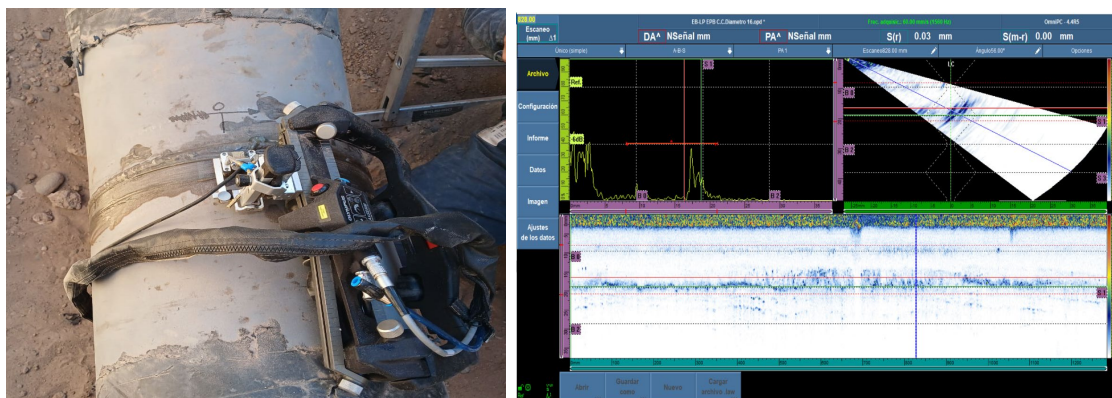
PAUT: INDICACIONES EN SOLDADURA
